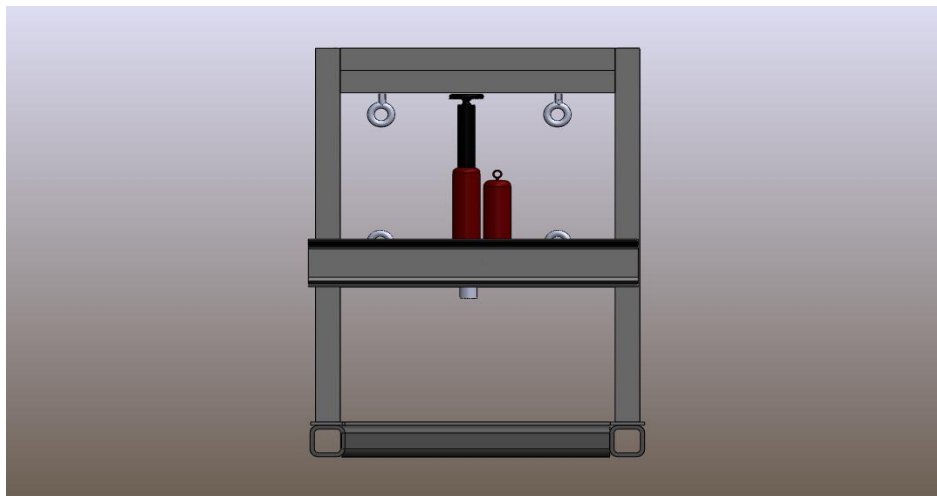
Ensamblaje en SolidWorks vista Isométrica.
